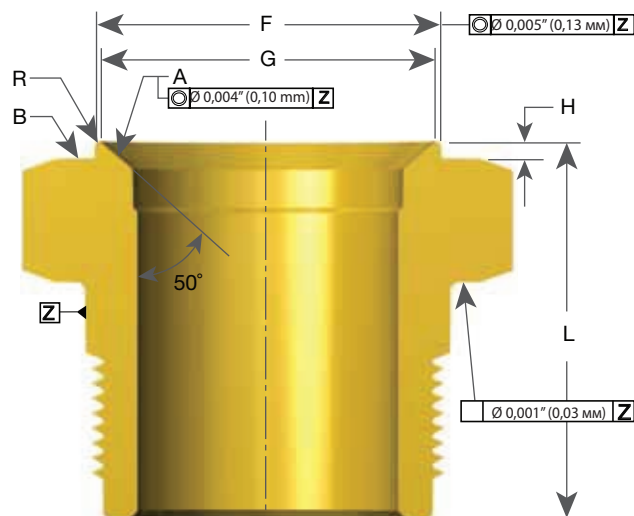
Седло с уплотнительным кольцом сопла (DA)
